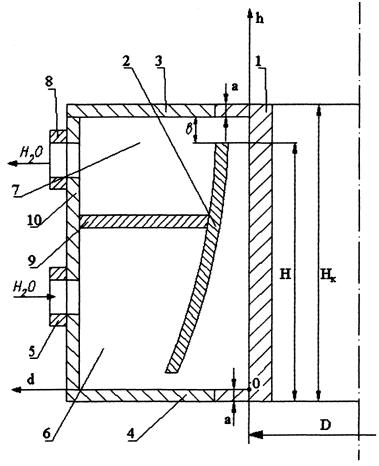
Кристаллизатор с переменным кольцевым канал: 1 — рубашка; 2 — экран; 3 — верхний фланец; 4 — нижний фланец; 5 — подводящий патрубок; 6 — нижний коллектор; 7 — верхний коллектор; 8 — отводящий патрубок
